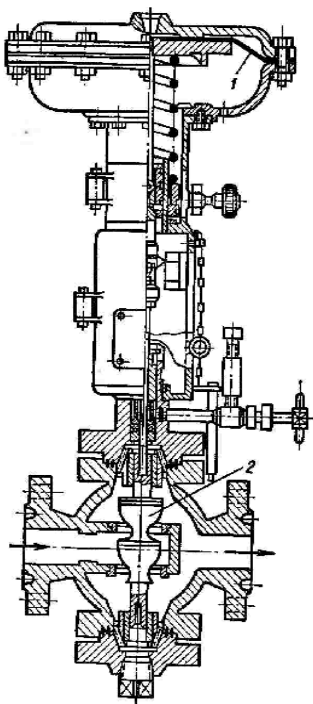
Пневматический исполнительный механизм мембранного типа
